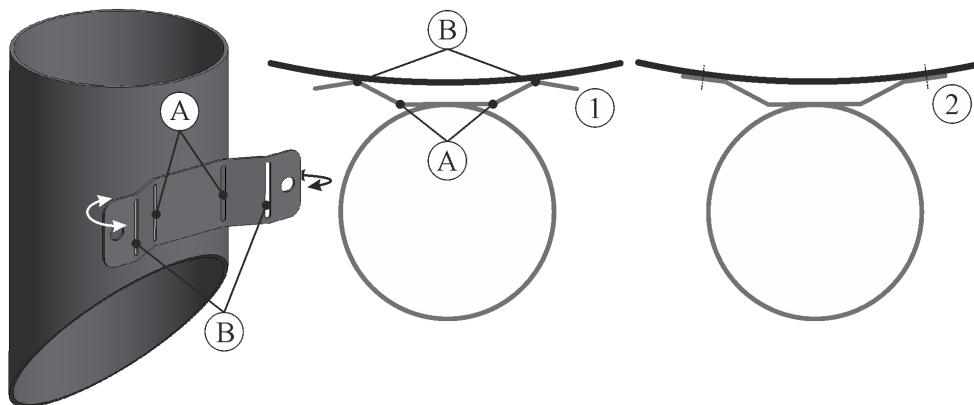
Регулировка крепления перепускного патрубка (примерный рисунок)
